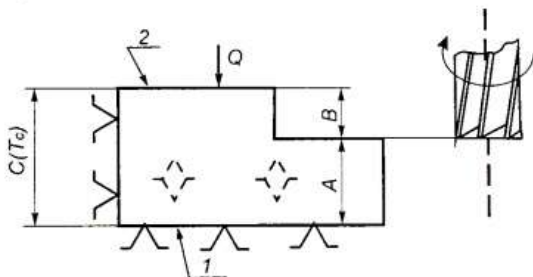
Похибка базування при базуванні деталі на площину
